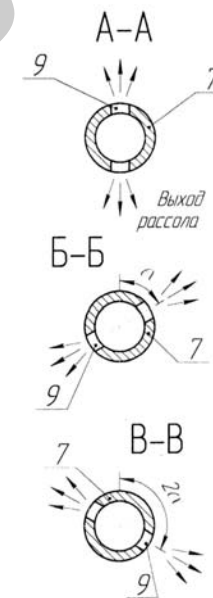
Схема расположения отверстий 9 в корпусе иглы 7 для выхода рассола
